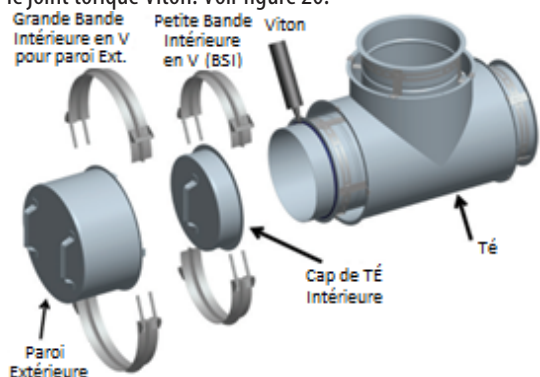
Étape 1 (uniquement pour une installation horizontale) Installation du TC
